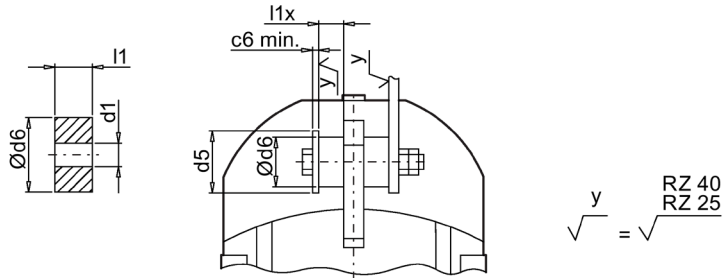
Montagevorschlag für Drehmomentstütze an F.29 - F.189
